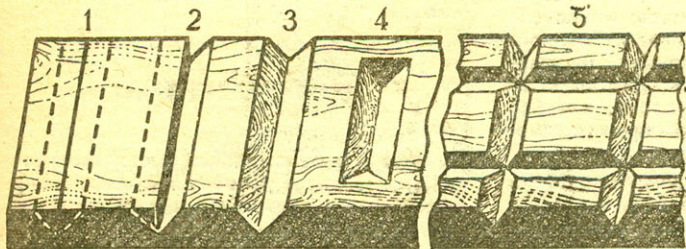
Тренировочное выполнение углублений: 1 — разметка, 2 — выборка половины, 3 — выборка всего сквозного углубления, 4 — «закрытое» углубление, 5 — выборка квадрата.
